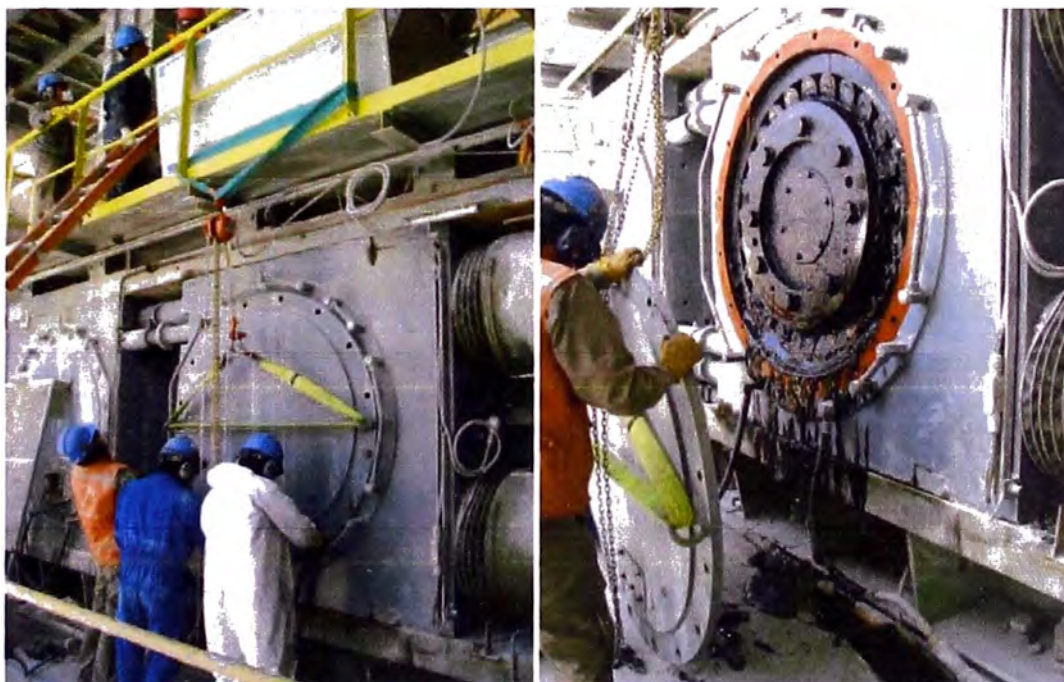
Inspección del estado de rodamiento exterior (B) de HPGR N°31.
